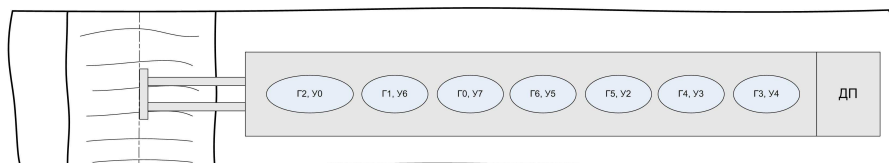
Схема расположения механоакустического блока МАБ1Д относительно сварного шва.
